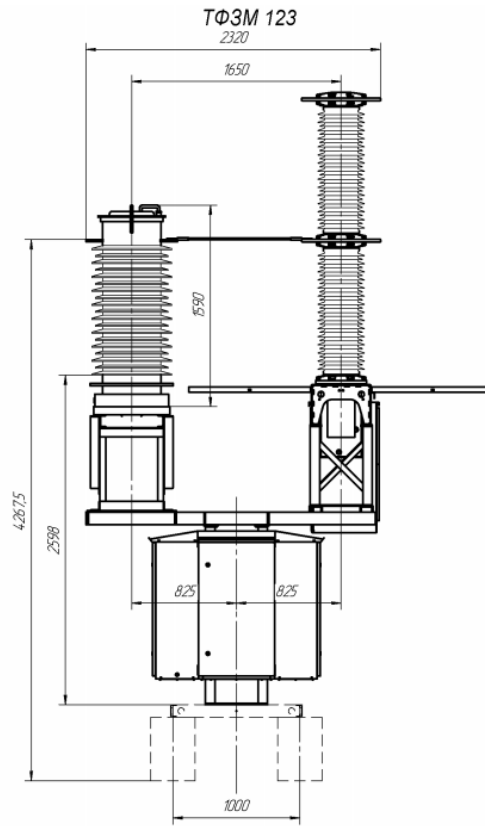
Габаритные, установочные и присоединительные размеры выключателя вакуумного ВРС-110 с трансформатором тока ТФЗМ 123
